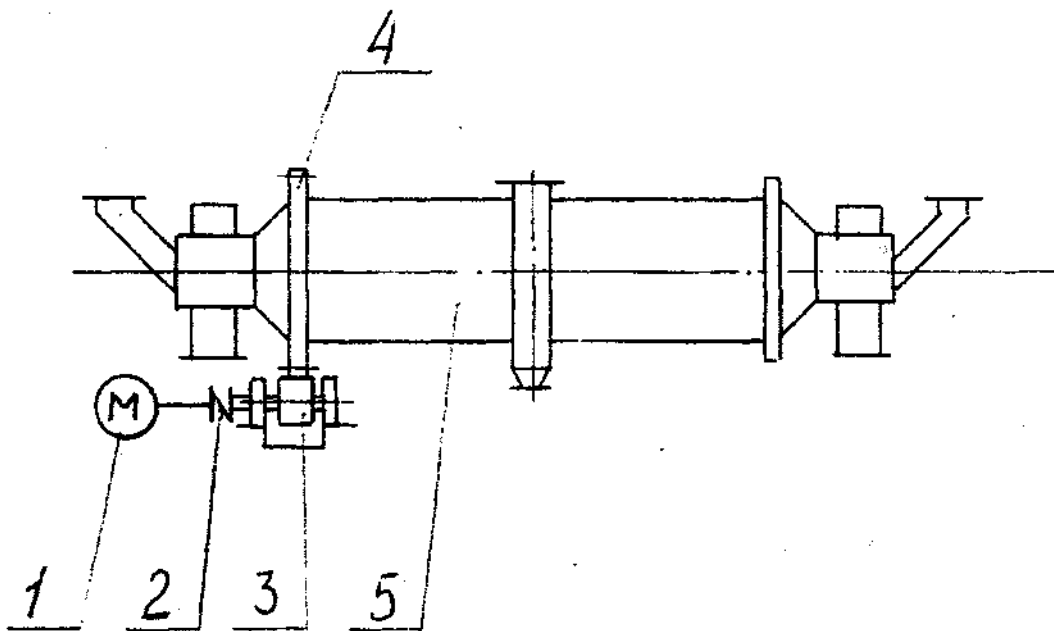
Кінематична схема приводу кульового млина 1 - електродвигун; 2 - муфта; 3 - приводна шестерня; 4 - ведене зубчасте колесо; 5 - барабан млина
